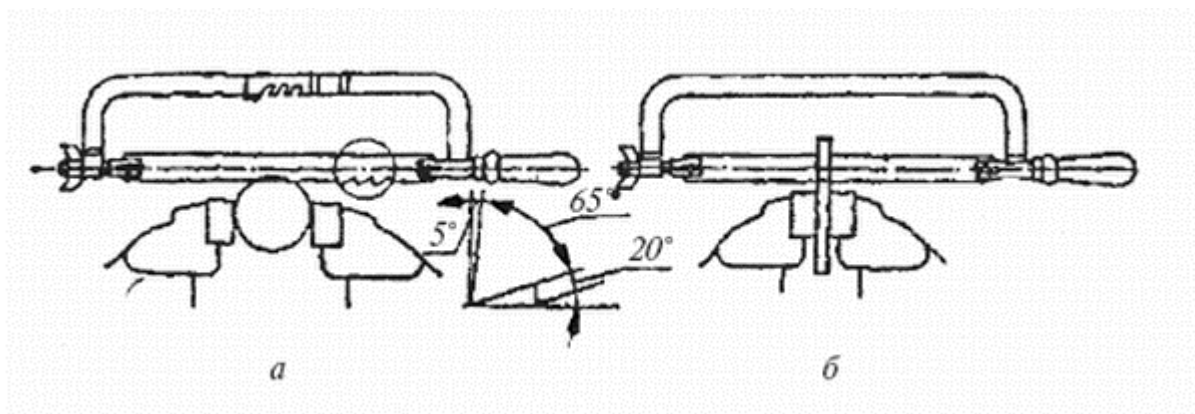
Ручные ножовки для металла а – регулируемая; б – нерегулируемая
